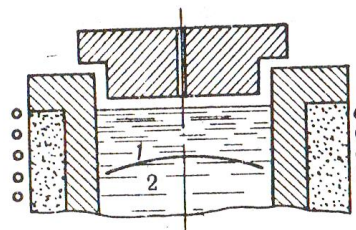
Графитовая крышка для подогрева шлака: 1- шлак; 2 – металл
